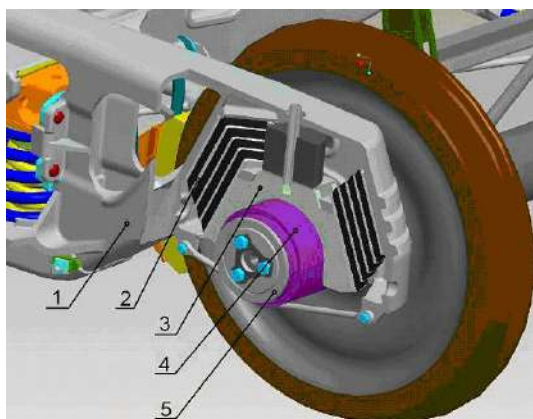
Буксовий вузол з гумометалевими пружинами шевронного типу
